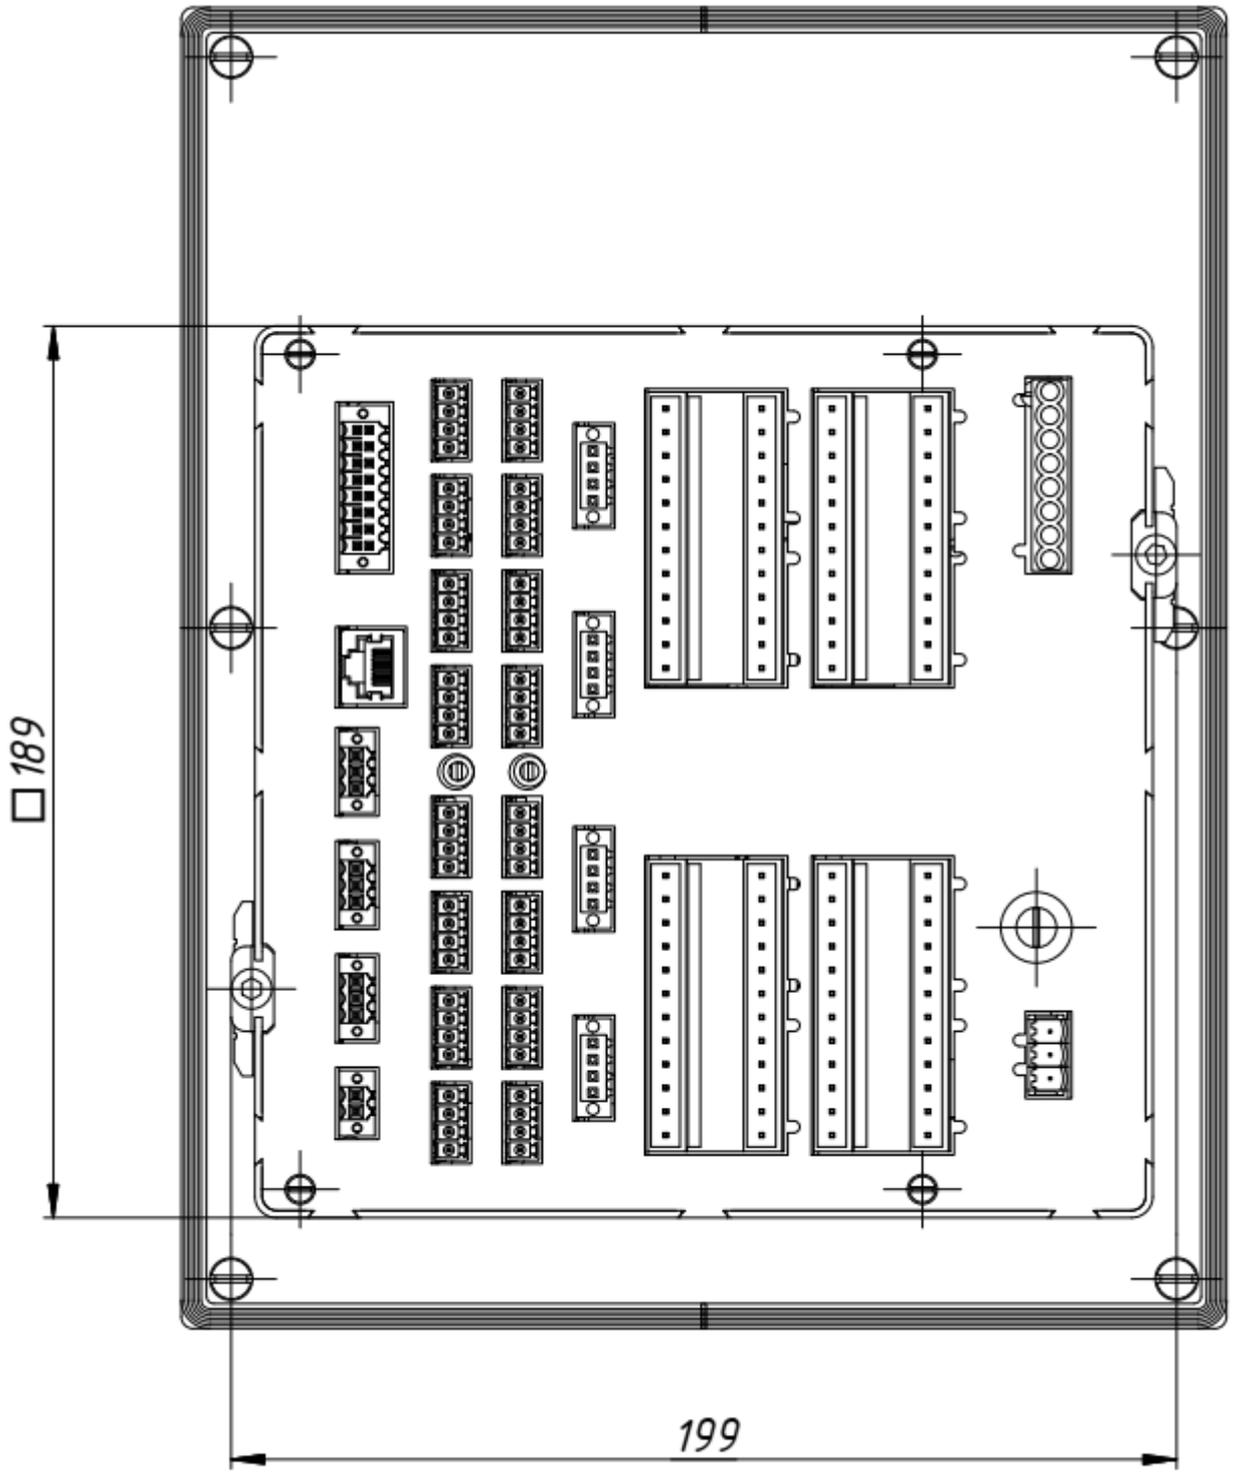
Габаритный чертёж прибора в исполнении Ф1772–4, вид сзади
